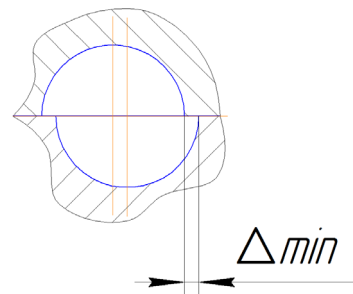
Умови кріплення валу турбіни і робочого колеса
